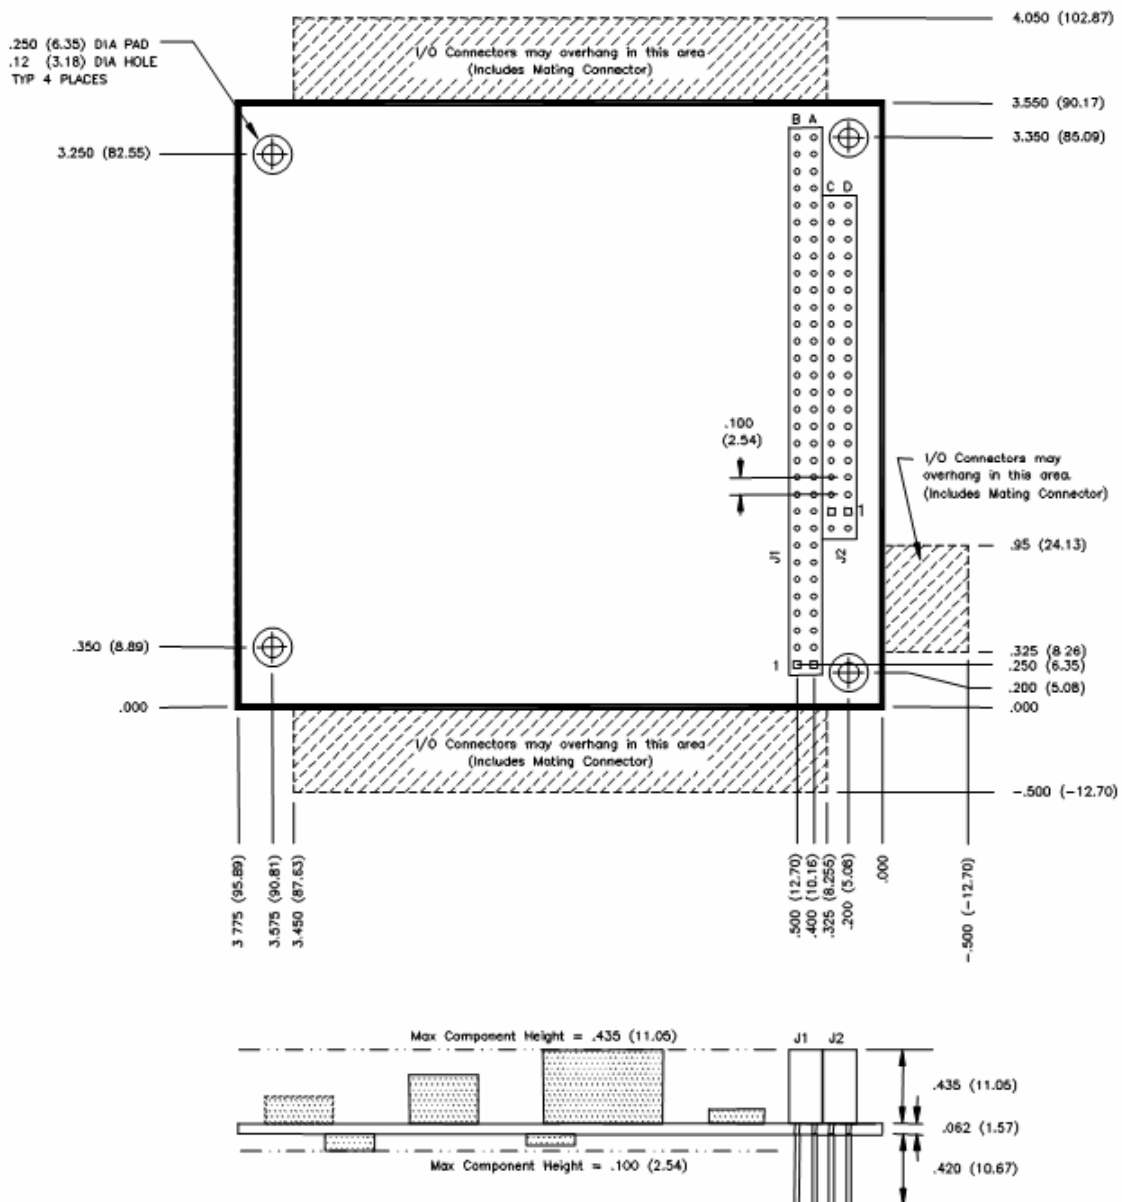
Dimensiones del módulo PC/104 en 8 y 16 bits
